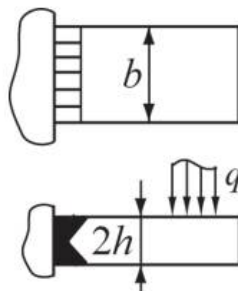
Сварное соединение в прямоугольной пластине
